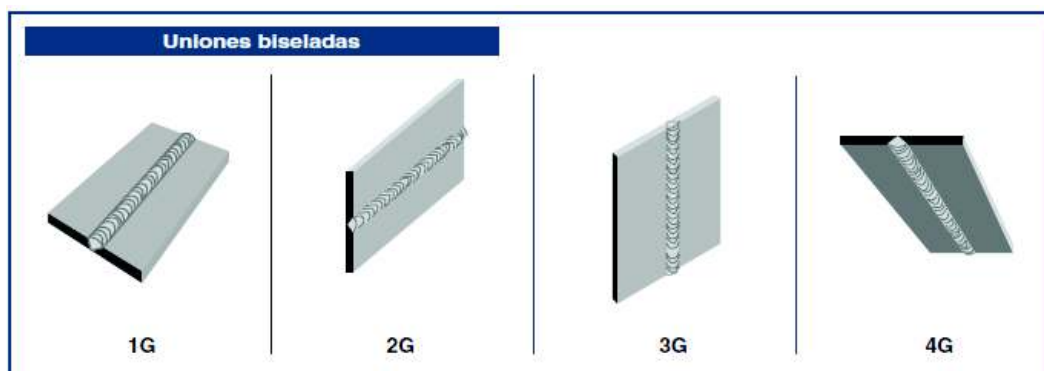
Posiciones de soldadura para uniones de bisel⁴⁶
